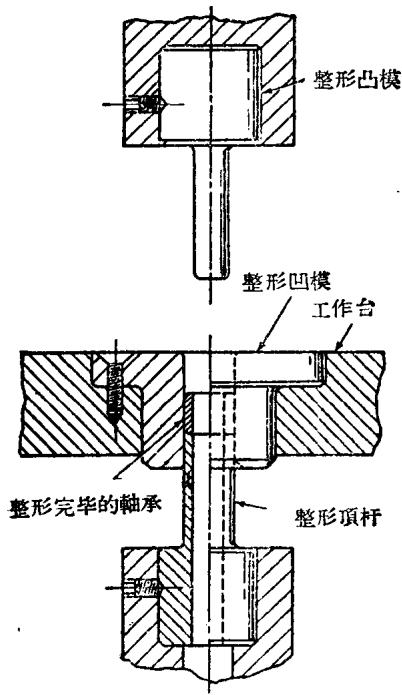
当单纯的压制和烧结不能取得某些尺寸公差时，通常即在烧结后进行整形。图中即为用于一个需要精密的外径与孔径尺寸的圆筒状工件的模具。由上凸模贴紧工件的内孔将工件压入外径整形凹模中，当工件停正在下方的顶杆面上时，凸模继续压进而完成内孔的整形。然后抽除凸模，待下方顶杆上升到工作台平面而顶出工件。
